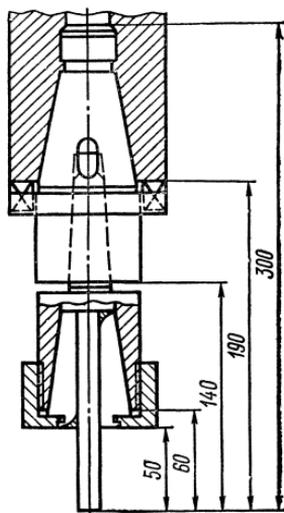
Цанговый патрон для крепления концевых фрез
